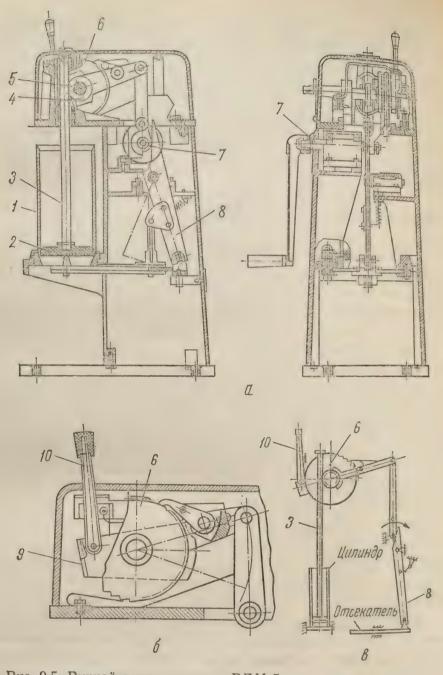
Ручной делитель масла РДМ-5: a, 6 — общий вид; B — кинематическая схема
